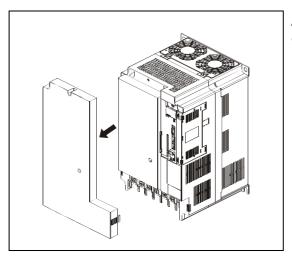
Schritt (2): Entfernen der Frontabdeckung
